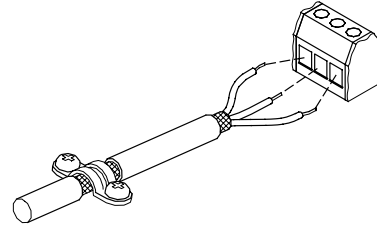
Соединение оплетки и проводов экранированного кабеля с колодкой
